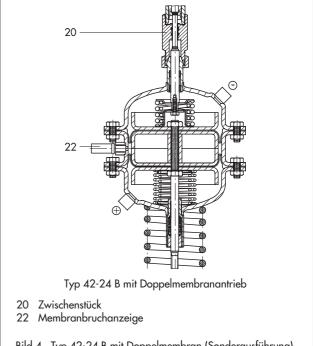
· Typ 42-24 B mit Doppelmembran (Sonderausführung)
